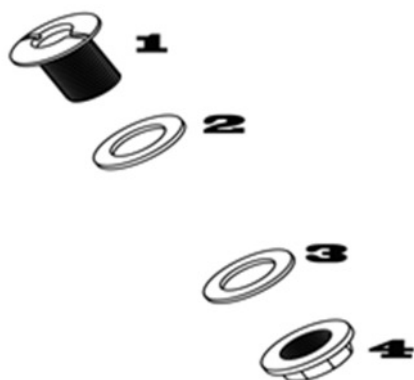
Втулка или резьбовая пробка (стекло находится между уплотнительным кольцом 3 и резиновым кольцом 2)
